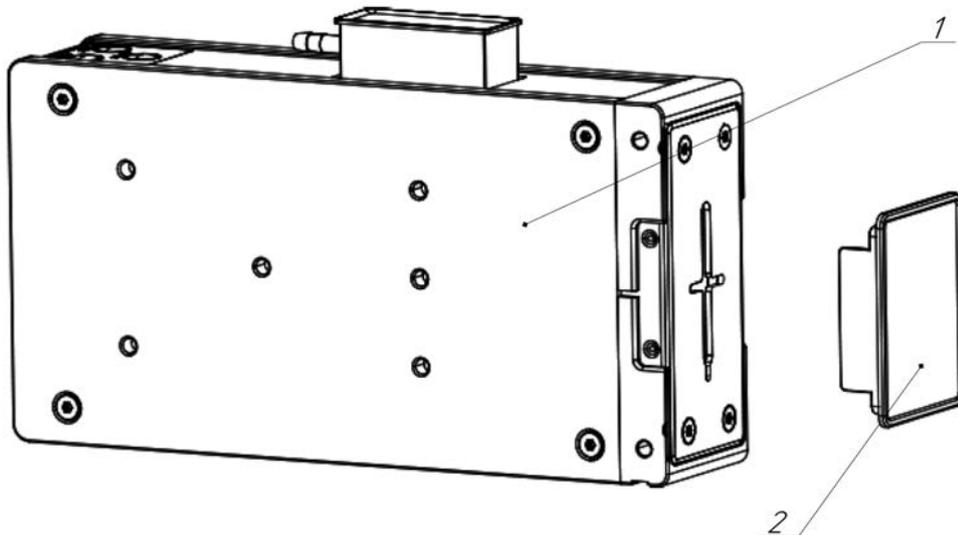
Печатающая головка и защитная крышка. Условные обозначения: 1 — печатающая головка; 2 — защитная крышка.
